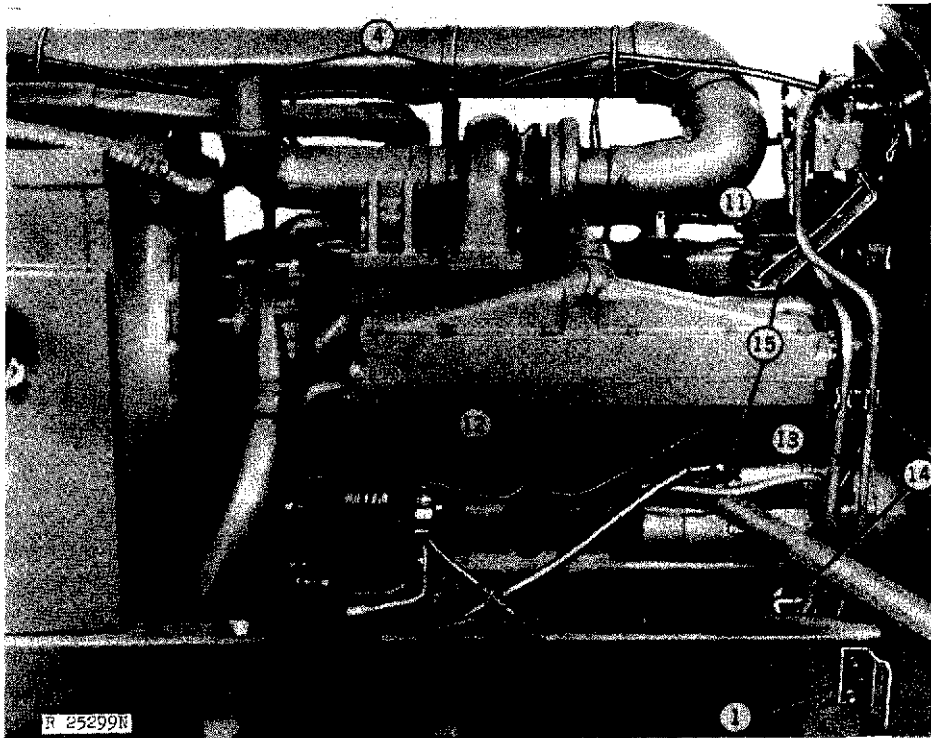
Pasos de Separación del Lado Izquierdo (8630)
